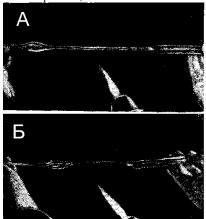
Растягивание заготовки: а —при равномерном вращении заготовки "плечики" получаются симметричными и одинаковыми; б — при рывке или неравномерном вращении "плечики" получаются неправильной формы, заготовка непригодна для дальнейшей обработки.
